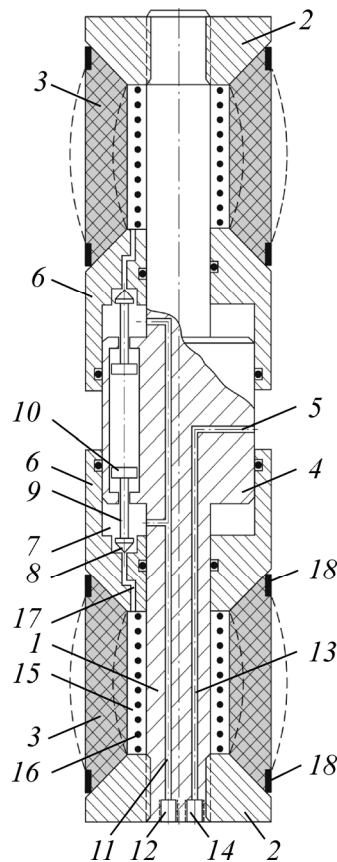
Скважинный зонд (патент 2652407 РФ): 1 — корпус; 2 — конические гайки; 3 — уплотнительные элементы; 4 — неподвижный шток; 5 — отверстие в штоке; 6 — цилиндры; 7 — рабочие полости; 8 — клапаны; 9 — штоки; 10 — хвостовики; 11, 13, 17 — каналы; 12, 14 — гнезда; 15 — полости под уплотнительными элементами; 16 — пружины; 18 — металлические кольца
